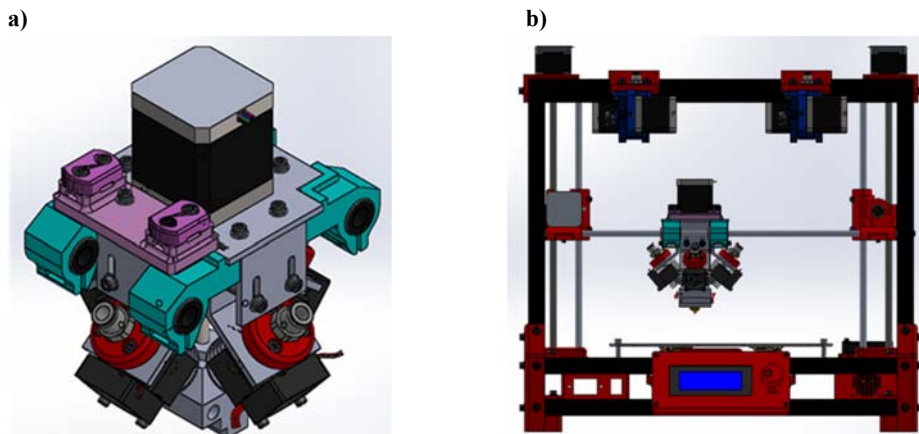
a) Capçal . b) Vista CAD frontal del capçal muntat a la impressora 3D. Font: [319].
